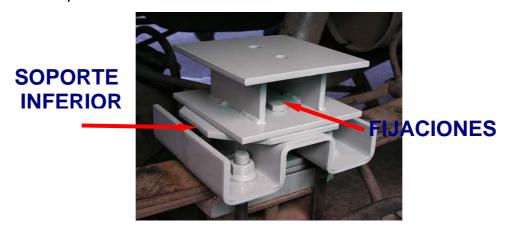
7. Montaje del elevador. Vista tren trasero lado derecho. Perspectiva
